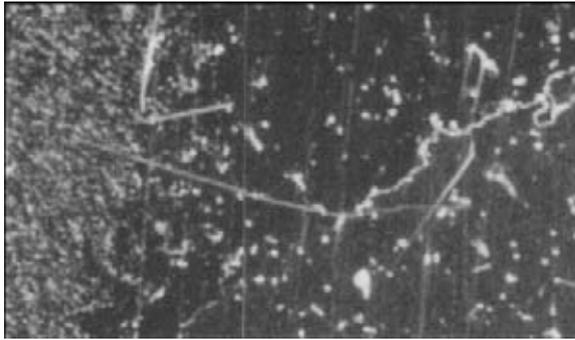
Микротрещины в металле ЗТВ сварного соединения из сплава инконель 738 (X100)
